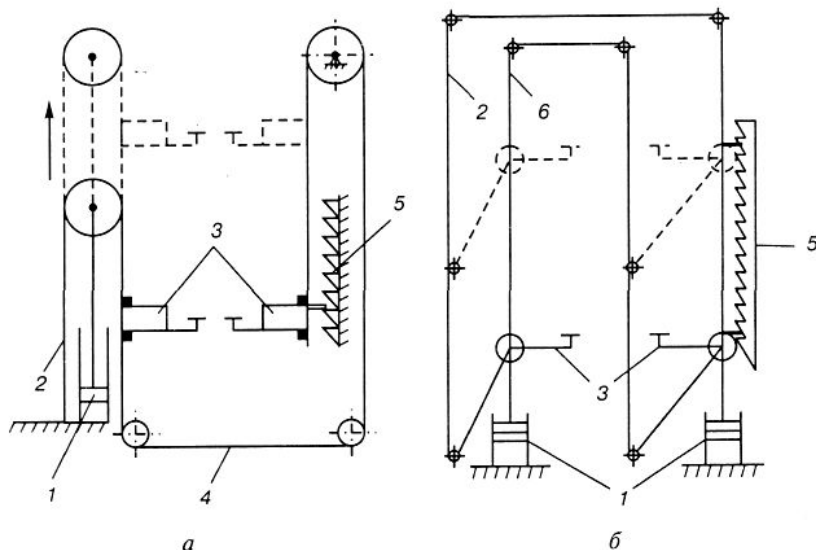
Типовые кинематические схемы привода кареток электрогидравлических двухстоечных подъемников: а — с одним гидроцилиндром; б — с двумя гидроцилиндрами; 1 — гидроцилиндр; 2 — приводной трос ведущей каретки; 3 — каретка; 4 — приводной трос ведомой каретки; 5 - стопорное устройство (храповое или клиновое); 6— синхронизирующий трос
